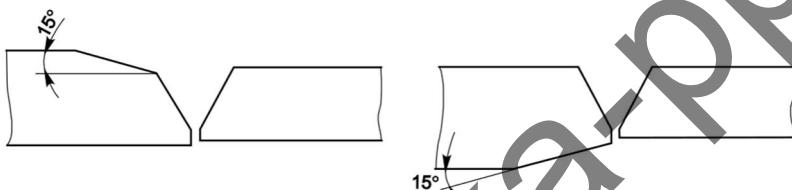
Подготовка стыка из разнотолщинных деталей
